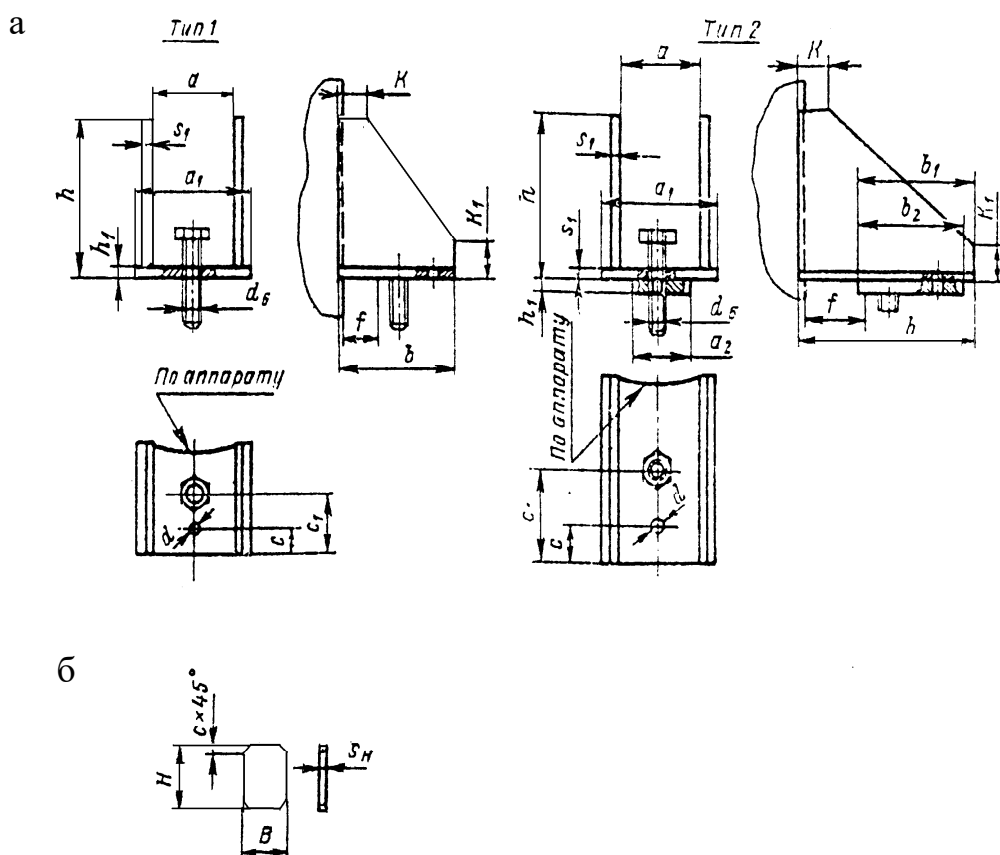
Конструкции стандартных опор (лап) для стальных сварных вертикальных цилиндрических аппаратов: а – типы 1 и 2; б – накладной лист
